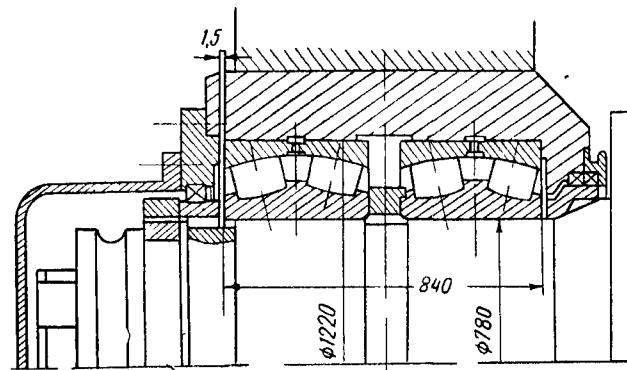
Сфероконические подшипники с конусной втулкой на шейке рабочего валка непрерывного проволочного стана 250
